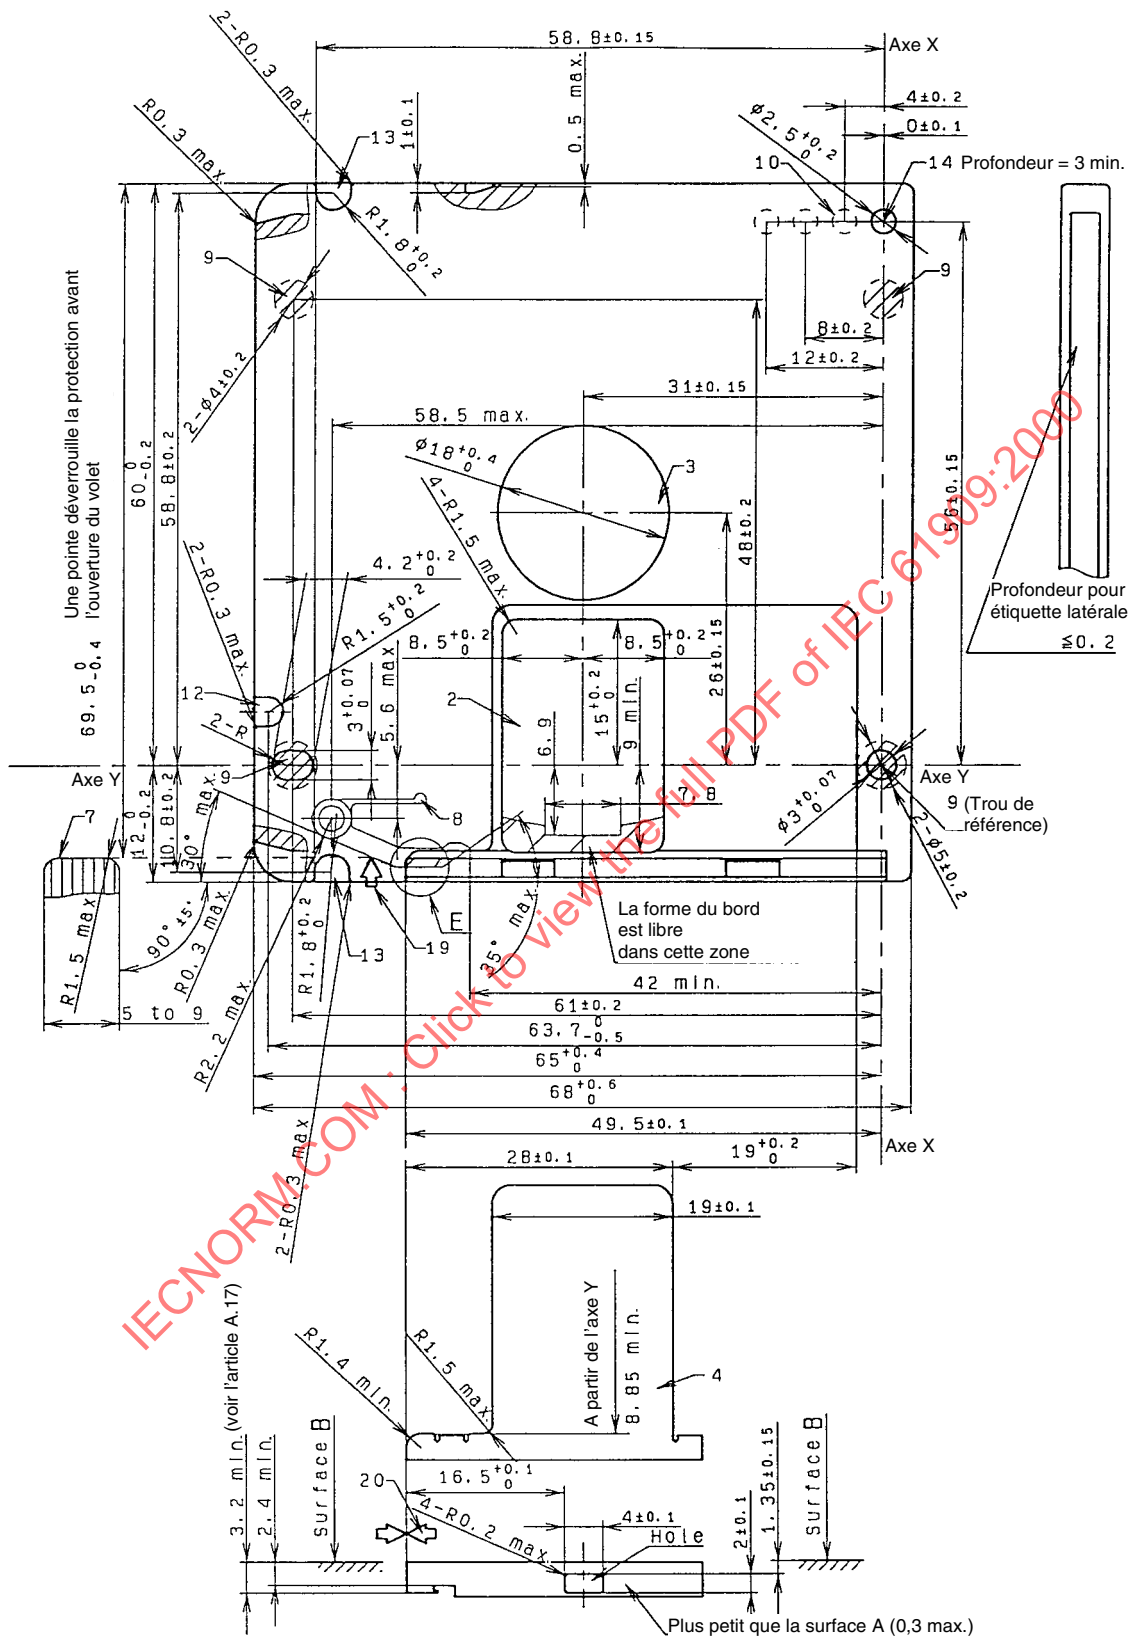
Vue supérieure et vue latérale de la cartouche du minidisque –
